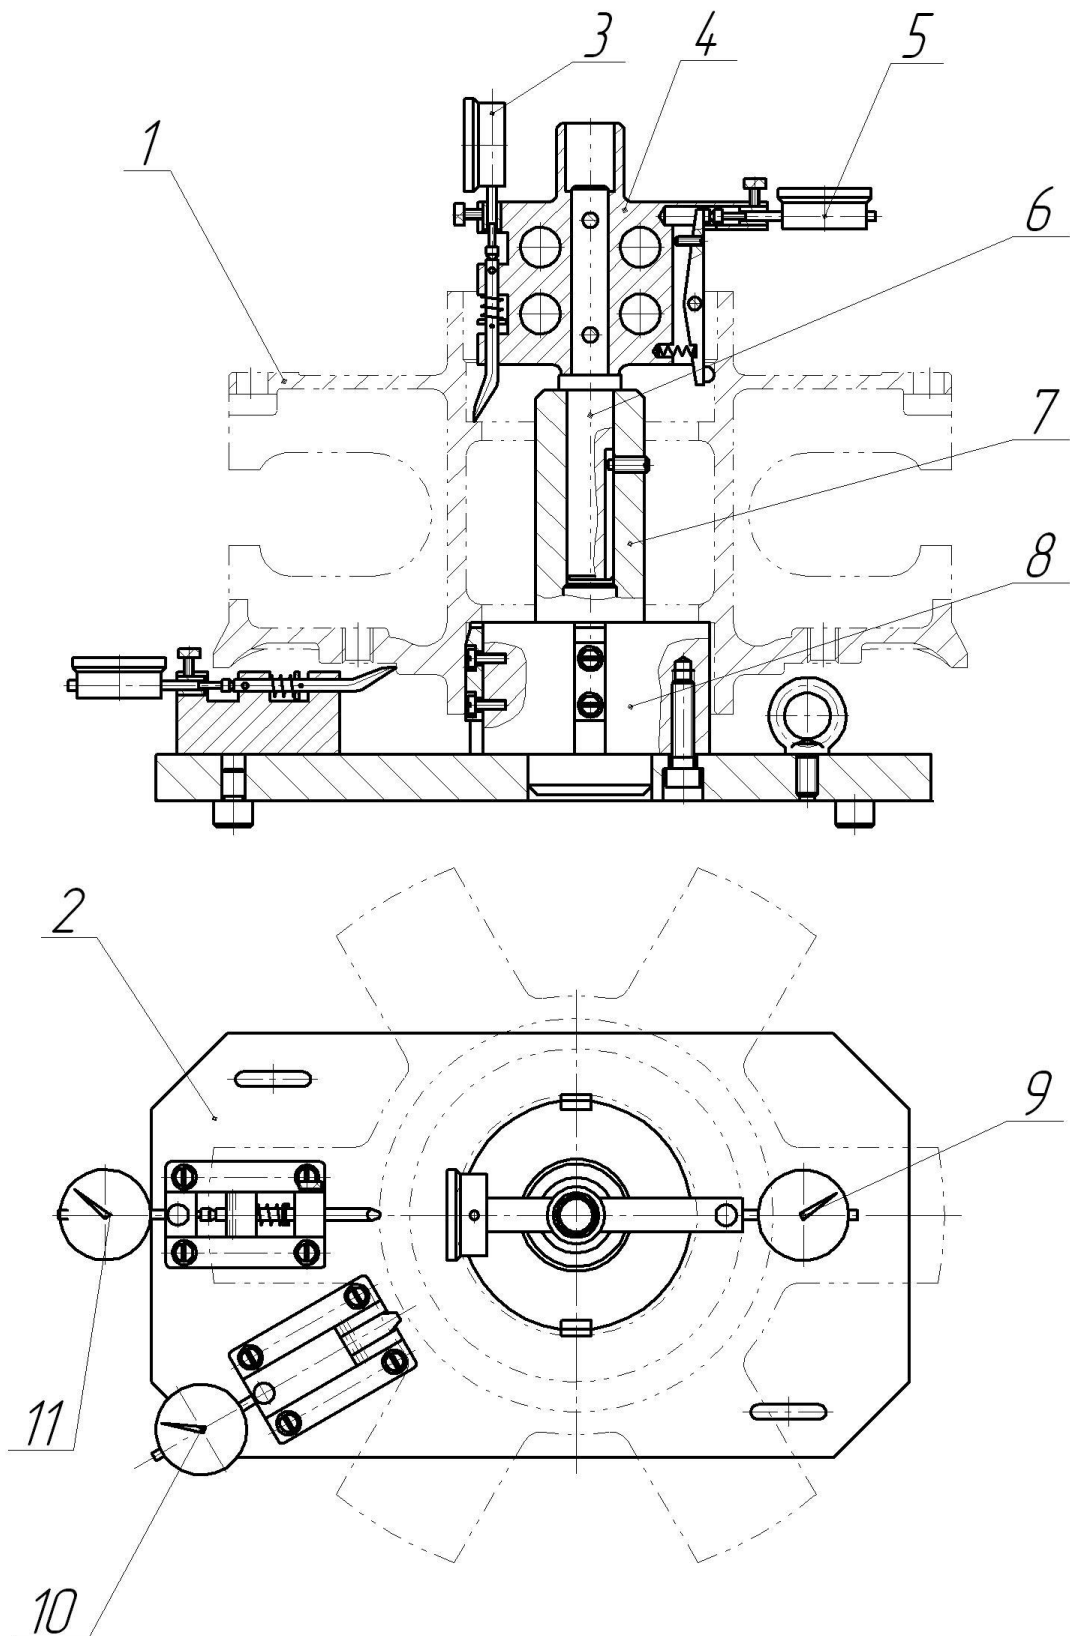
Пристрій для контролю технічного стану маточини колеса : 1 - маточина колеса; 2 - установочна плита; 3, 9, 10, 11 - перетворювач класу 2 ДСТУ; 4 - верхня цапфа; 6 - стійка (вісь); 7 – обойма; 8 – основа.
